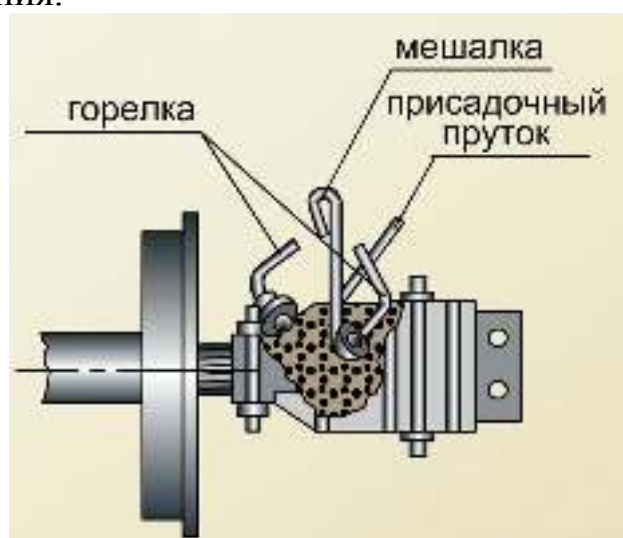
Оконцевание алюминиевых жил пластинами с использованием газовой сварки.
